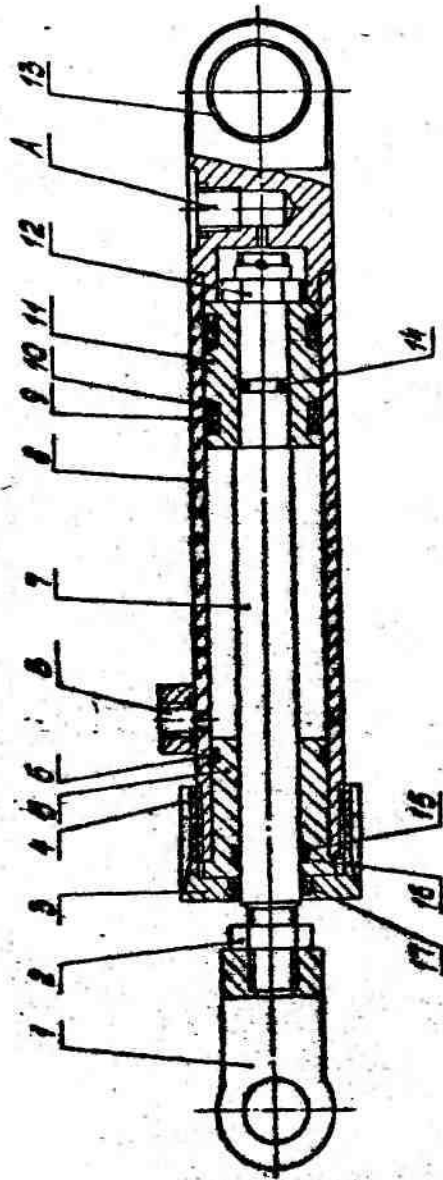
Гидроцилиндр механизма блокировки подрески
